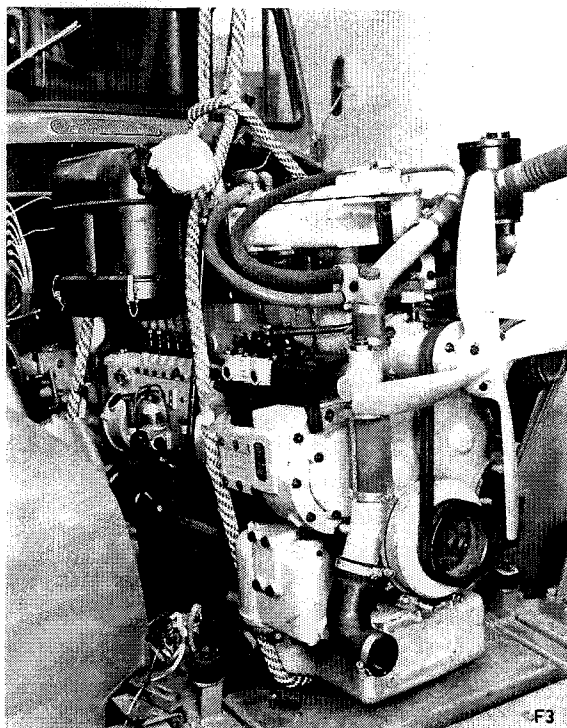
+4 Ausbau des Motors mit Kupplung und Getriebe aus dem Fahrzeug
